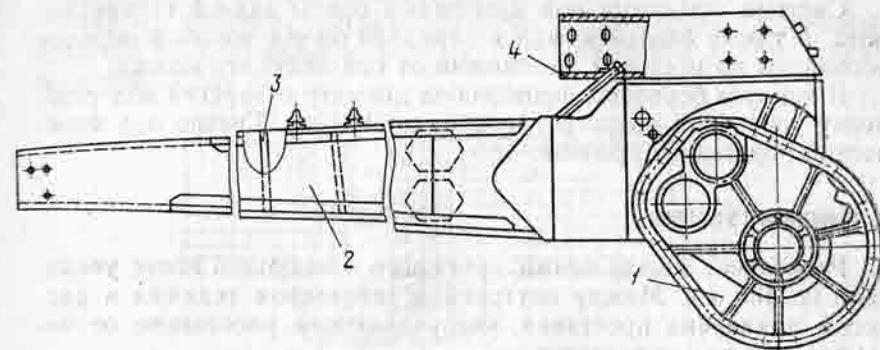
Корпус бортовых фрикционов с лонжеронами в сборе:
